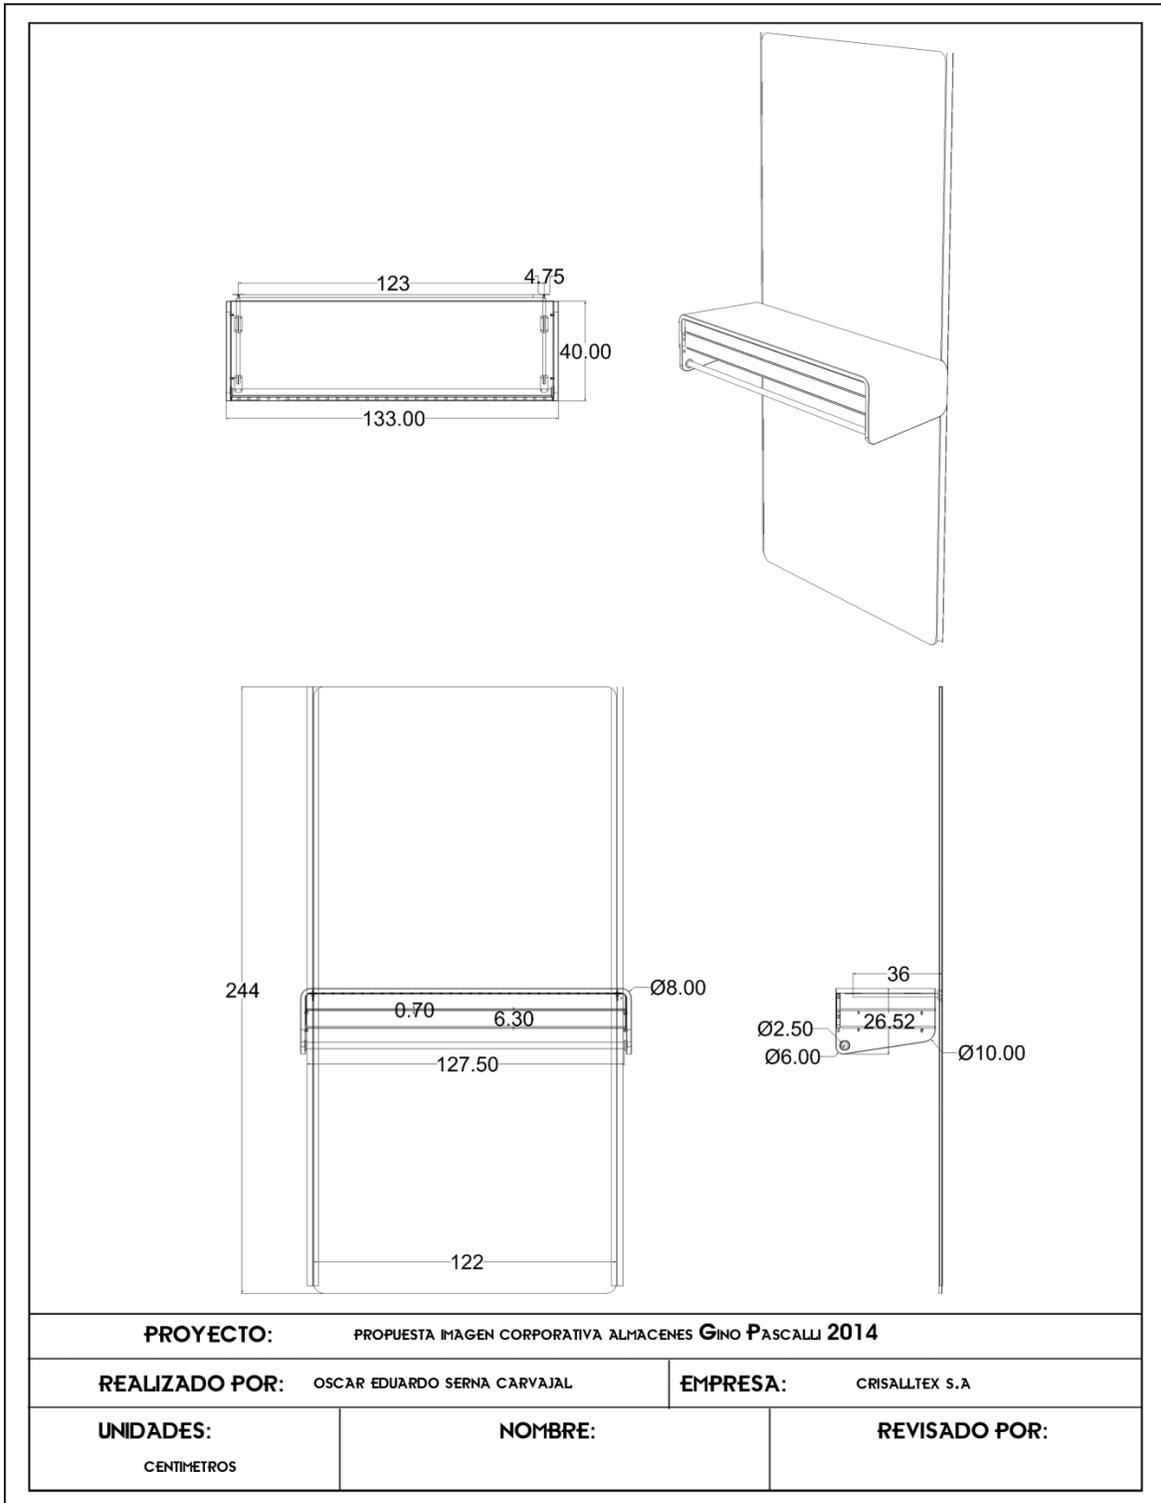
Planos Técnicos Entrepaños Sistema Drywall
